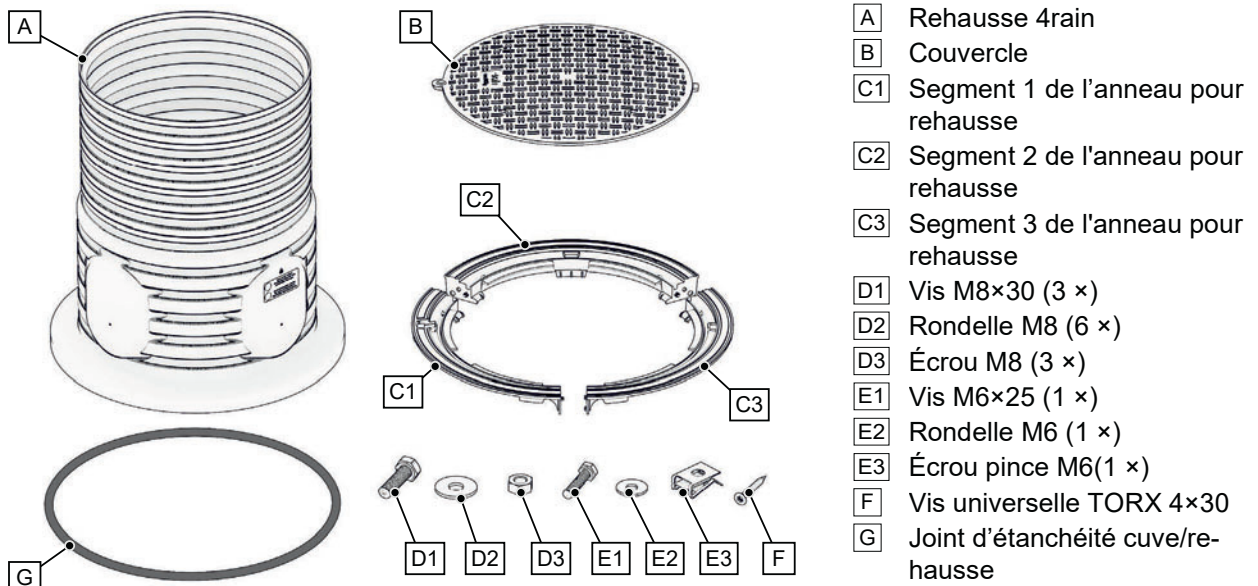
Rehausse 4rain et couvercle – Vue éclatée
